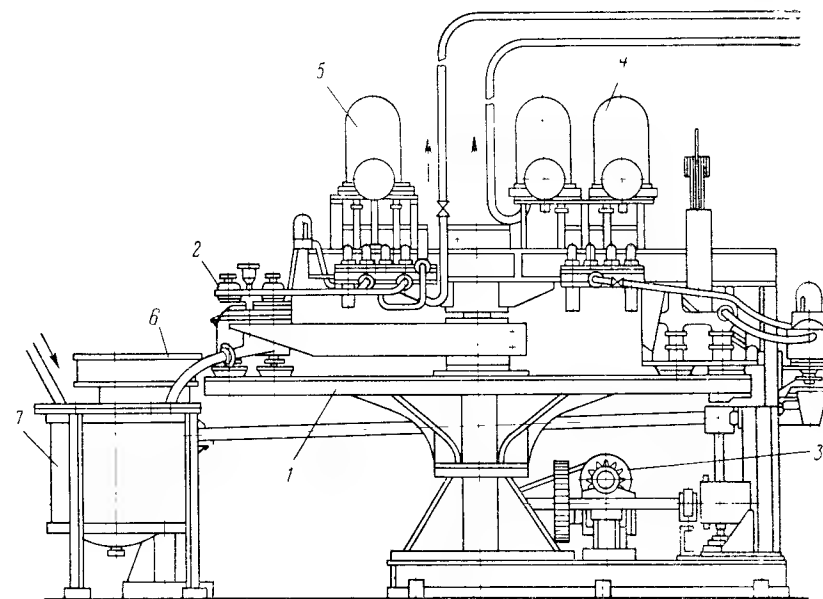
Четырехструйный полуавтомат для отливки чашек
